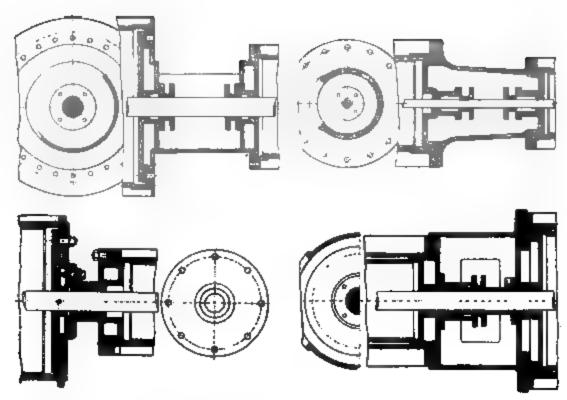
Verbindangsstücke. Fig. 1539-1542.
